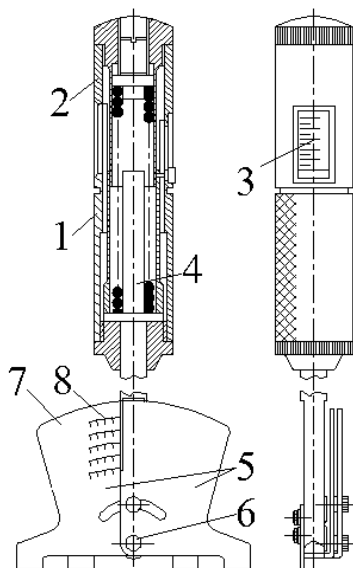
Приспособление КИ – 8920 для проверки натяжения ремней:
